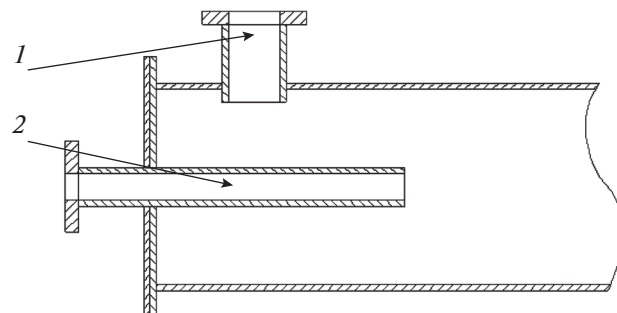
Трубчатый турбулентный реактор цилиндрического типа: 1 — патрубок ввода мономеров; 2 — патрубок ввода катализатора.
